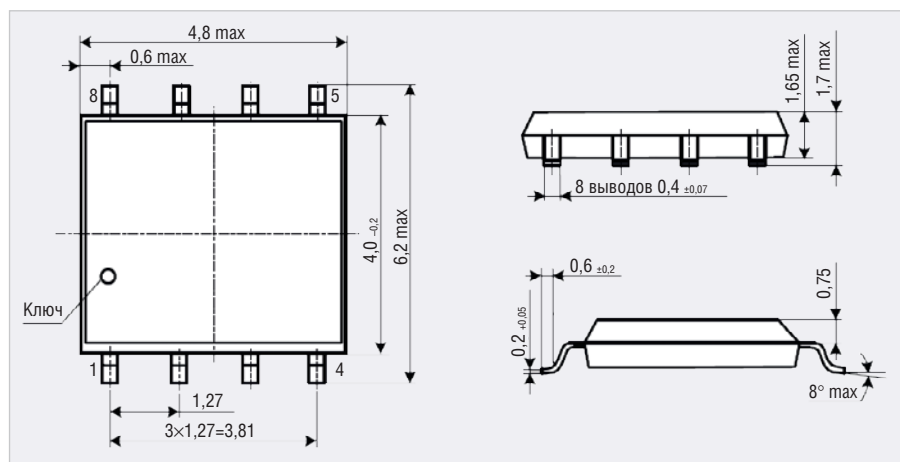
Чертёж корпуса SOIC-8 микросхемы K5559IH14ASI
